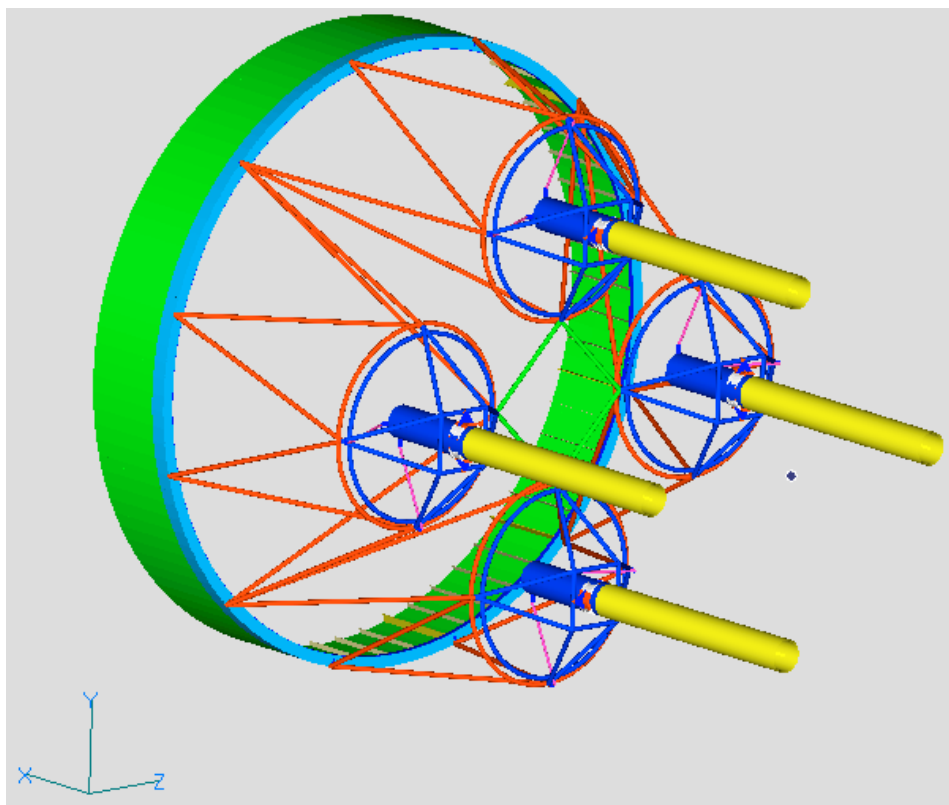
Ферменная конструкция крепления двигателя
